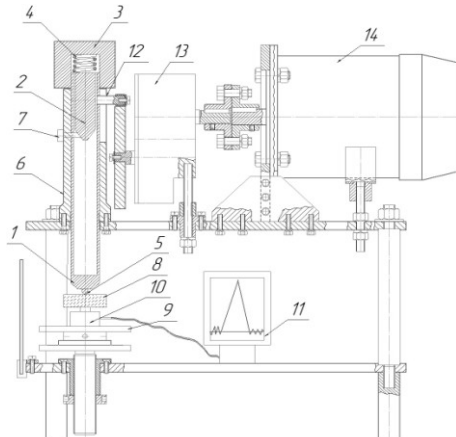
Принципиальная схема установки по разрушению анализируемых материалов: 1 – корпус модельного инструмента; 2 – вставка(и); 3 – крышка; 4 – пружина; 5 – индентор ($R_M = 3$ мм); 6 – направляющая труба; 7 – стопор; 8 – пластина породы или металла; 9 – установочная плита; 10 – датчик силы; 11 – аналого-цифровой преобразователь NI USB 6008; 12 – кулачок; 13 – редуктор; 14 – электродвигатель
